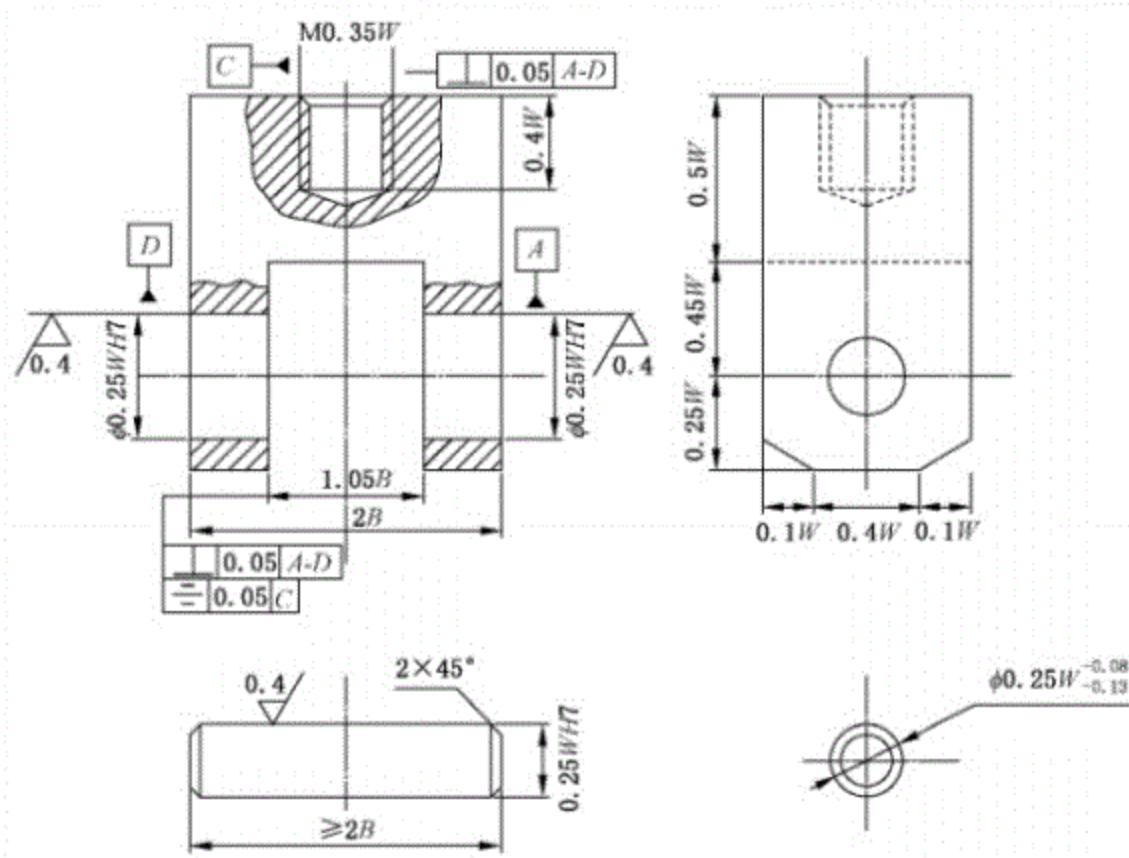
焊接接头疲劳裂纹扩展速率 CT 试样的 U型锁孔夹具
